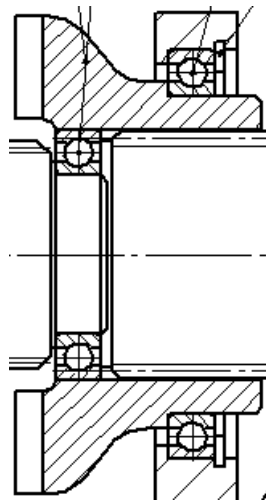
Общий вид шлицевого соединения полумуфты включения главной передачи и вала
